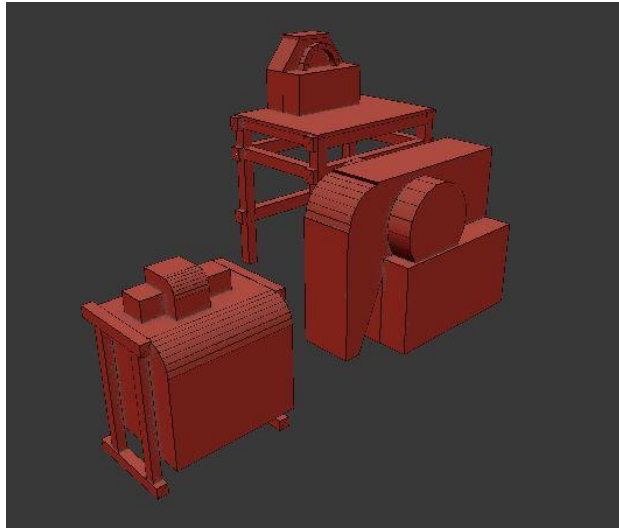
Modelado de la satinadora, en primer plano y la noria y la tarara al fondo.
